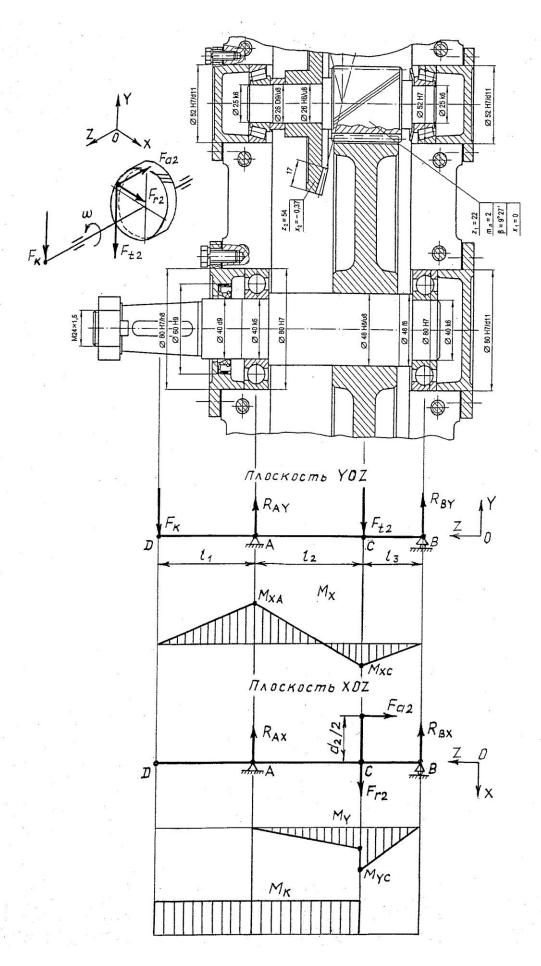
Расчётная схема тихоходного вала редуктора
